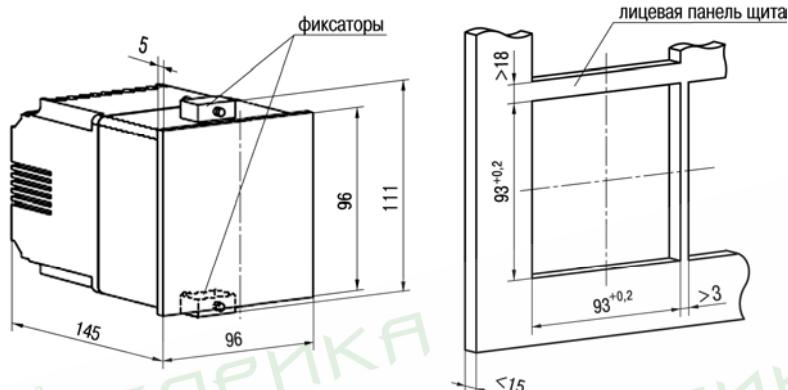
Габаритный чертеж прибора в корпусе Щ4
